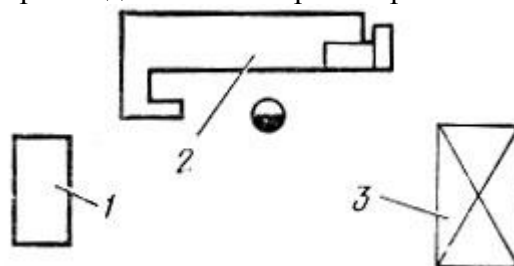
Планировка рабочего места столяра: 1 - инструментальный шкаф, 2 - столярный верстак, 3 - подстопное место для сборки изделия
